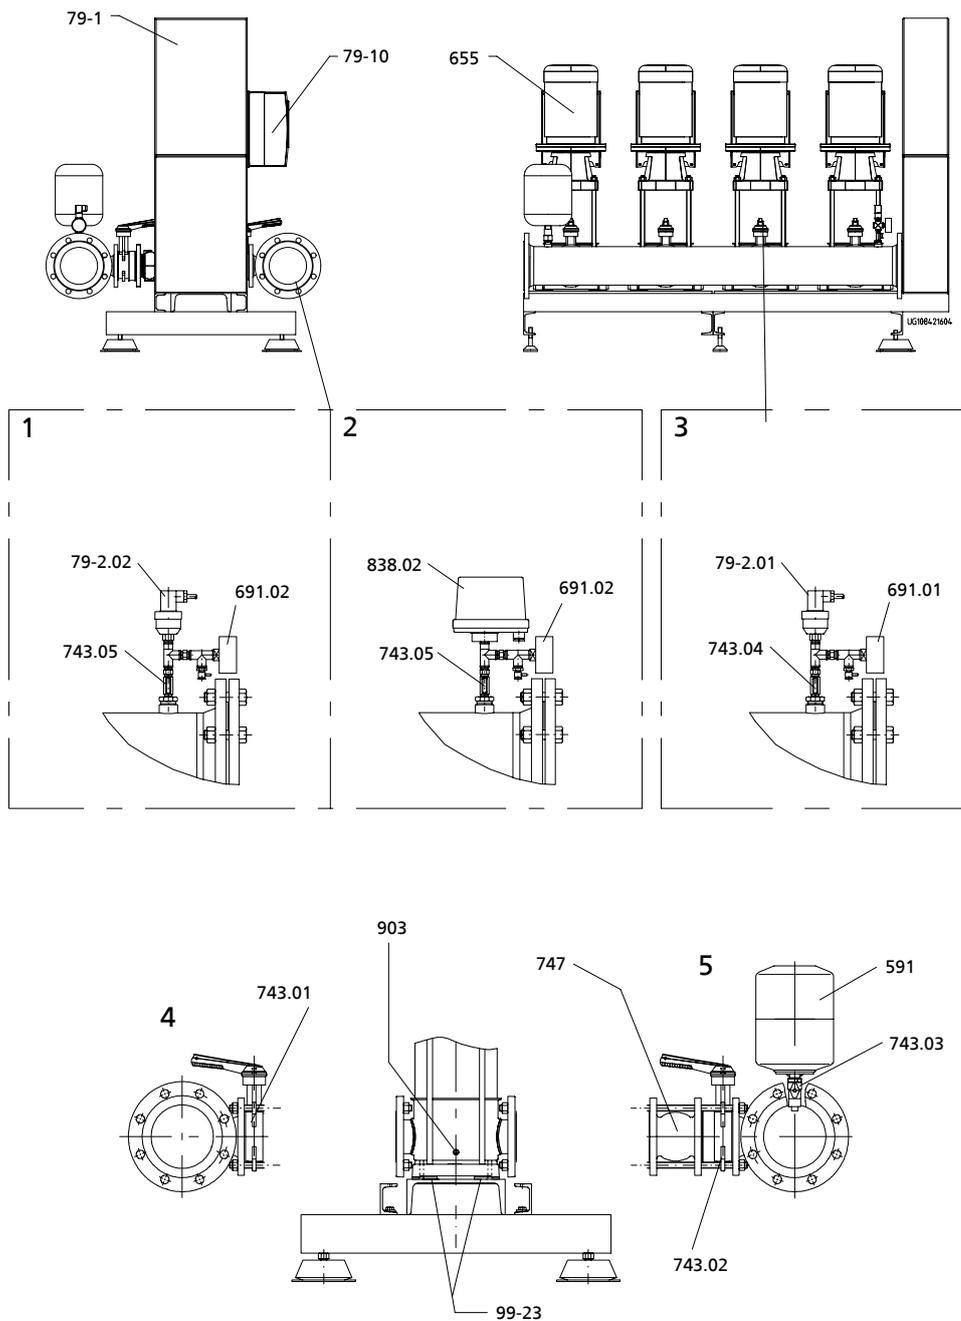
Сборный чертеж Hyamat SVP с Movitec 25, 40, 60, 90
